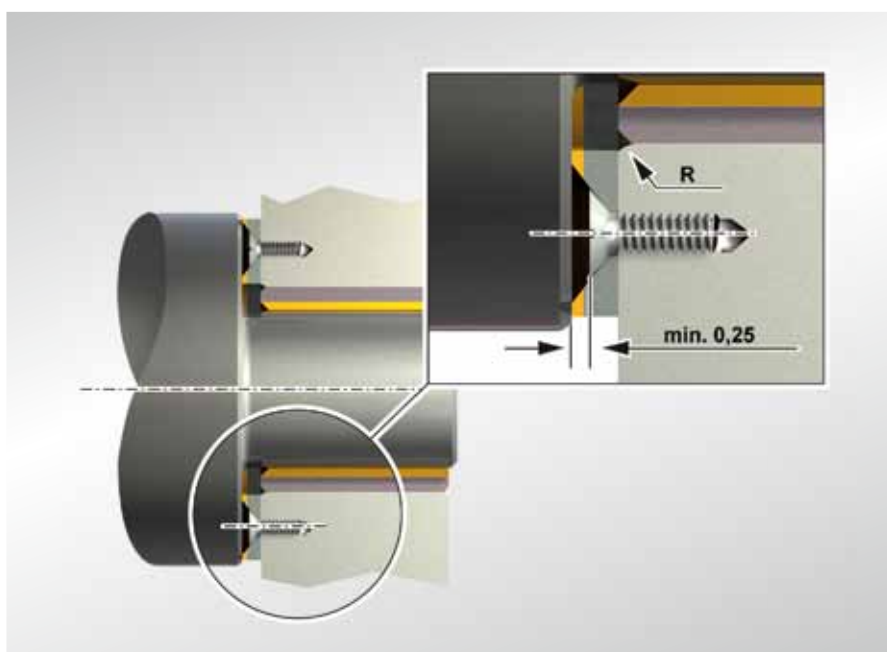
Befestigen einer Anlaufscheibe PAW ohne Ausnehmung im Gehäuse
